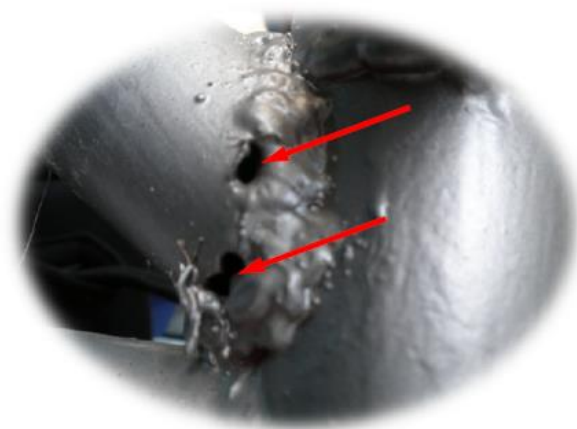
Mala soldadura amb penetració del material a soldar
